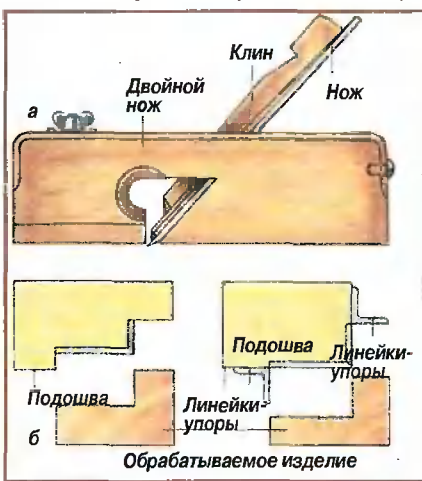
Фальцгубель: а — внешний вид; б — форма подошвы и профиль обрабатываемой детали.
